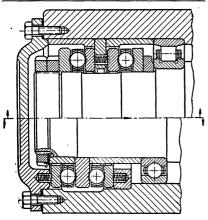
Установка пружин в узлах с двойным и двумя одинарными подшипниками
